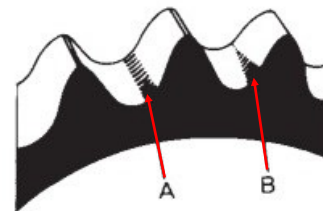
Zones à vérifier pour déceler l'usure de la roue dentée/
